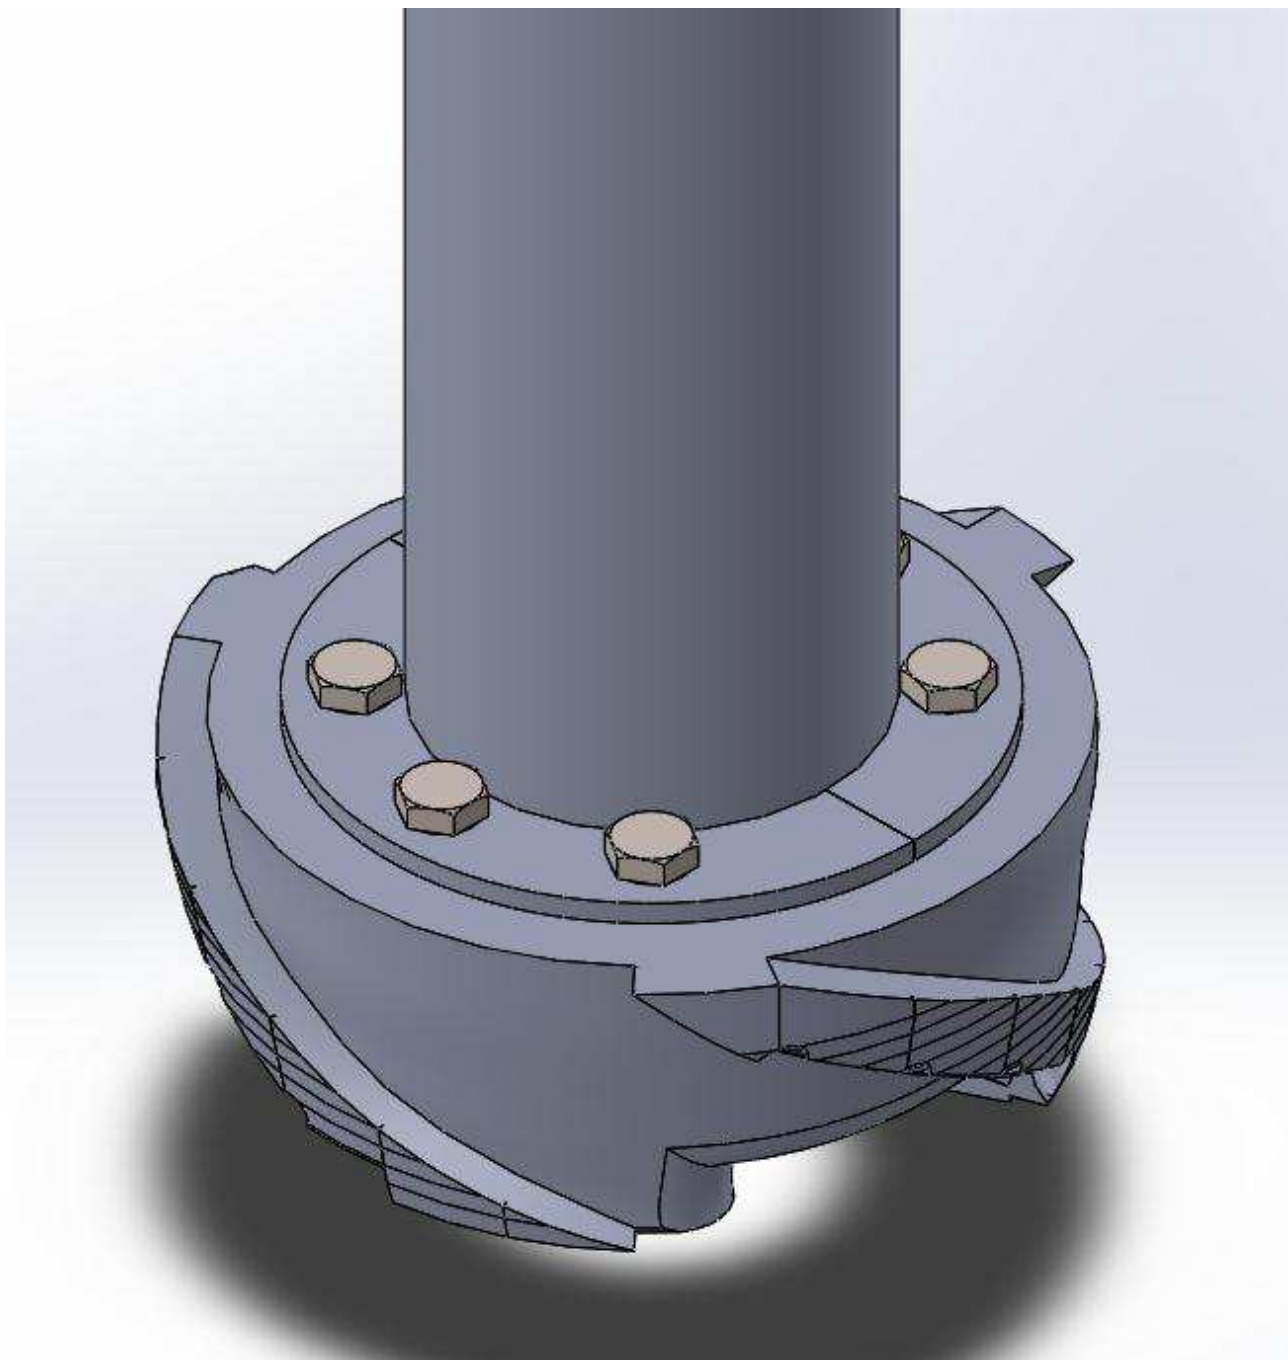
Штанга фрезерного оборудования в сборе
